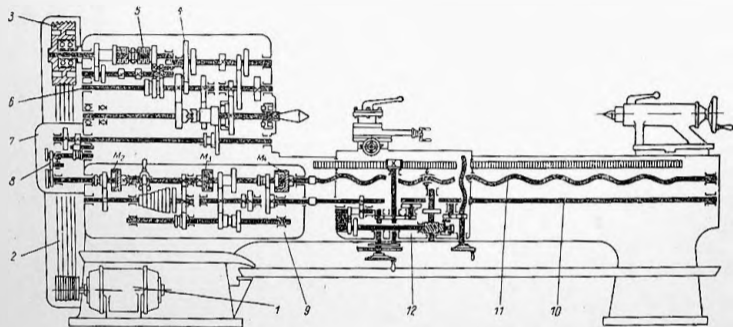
Schema cinematică a strungului 1A 62-S8, fabricat în R.P.R.:
